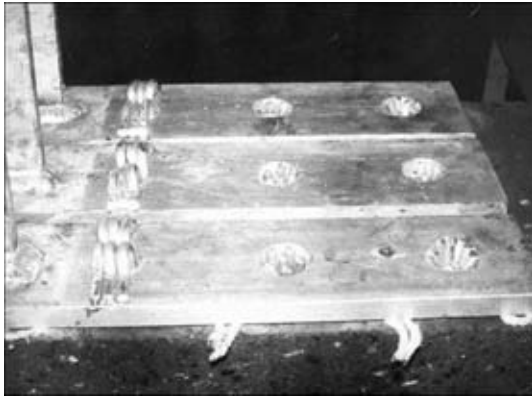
Элемент контактного узла печи Ачесона, подготовленный к монтажной сварке
